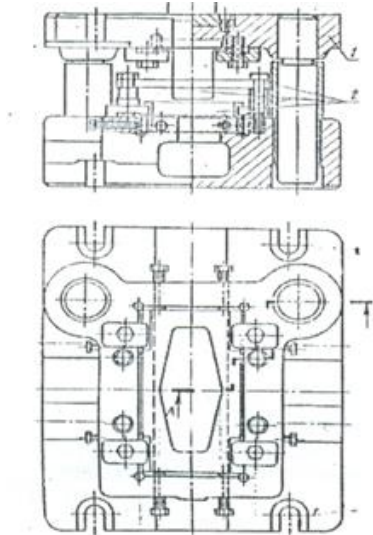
Компонівка блока універсального штампа для обрізки облою у поковок з подовженою віссю на кривошипних пресах
